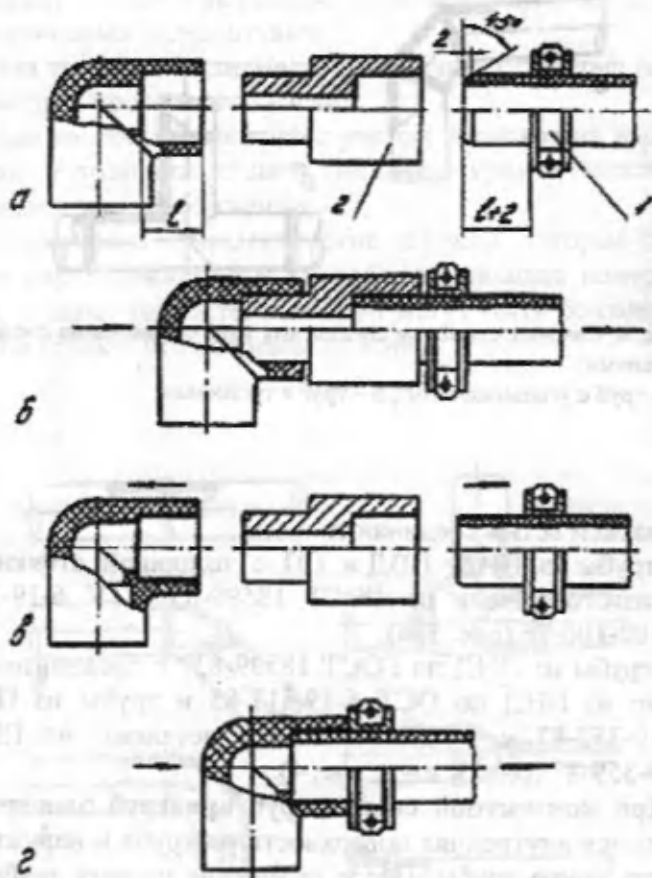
Последовательность процесса контактной сварки в раструб труб и соединительных деталей из ПВД:
